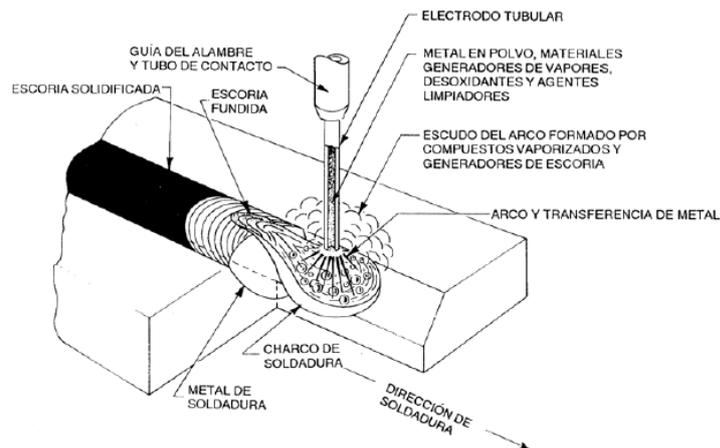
Soldadura FCAW con autoprotección
